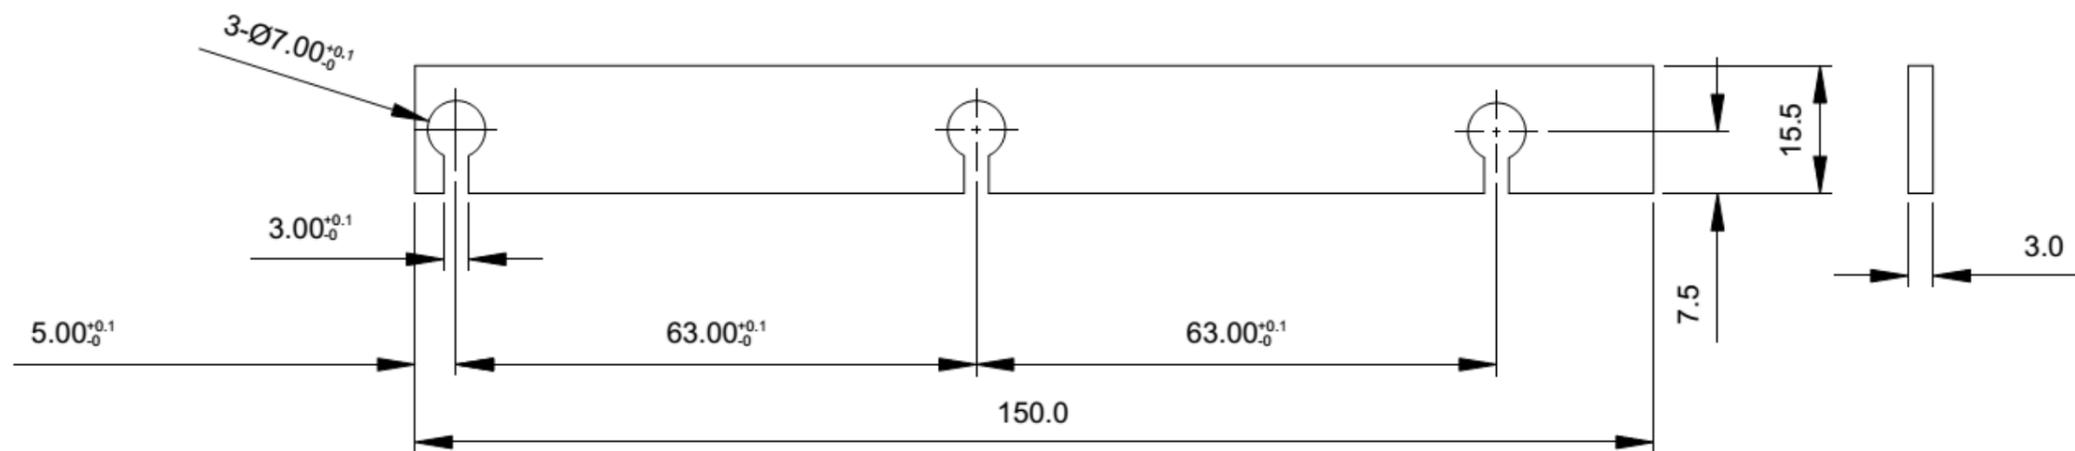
Gambar Kerja Rancangan Assembly Jig untuk Tool No. 5746-B4-1-A
